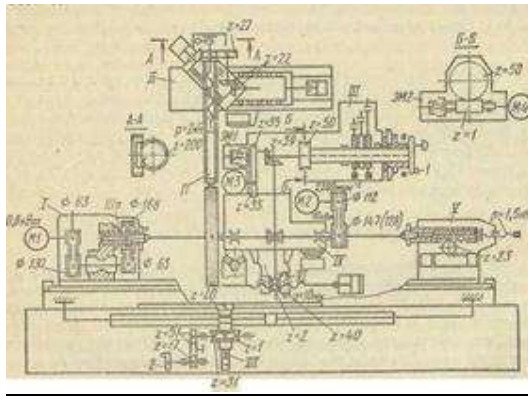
Кінематична схема круглошліфувального верстата 3М151: I - передня бабка; II - пристрій для редагування; III - механізм подач; IV - шліфувальна бабка; V - задня бабка; VI - механізм швидкого підведення; VII- механізм ручного переміщення столу
